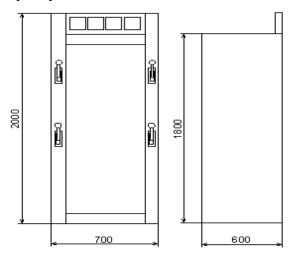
Конструкции и габаритные размеры ЩО-07
